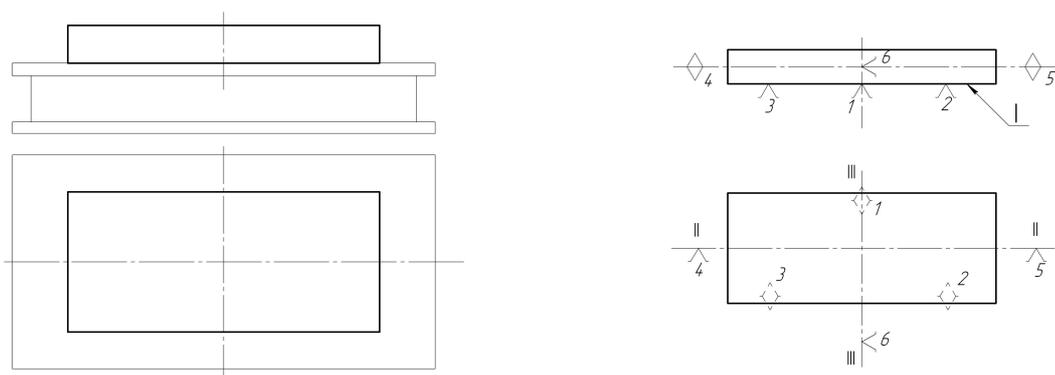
Установка заготовки по плоскости (на магнитной плите):
